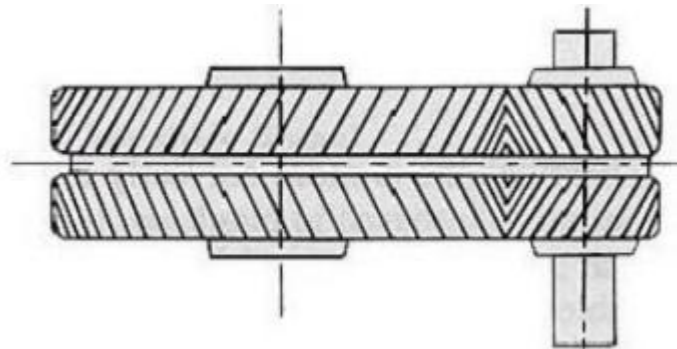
Engranajes dobles helicoidales. Los engranajes dobles son una combinación de hélice derecha e izquierda.
